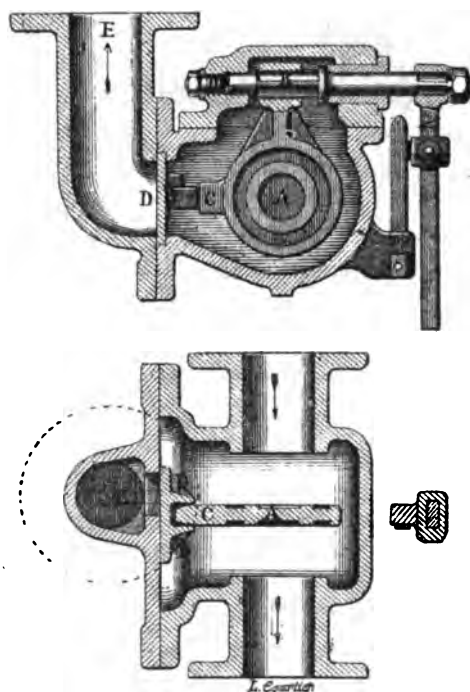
et 728. — Clapet obturateur de vapeur Vaultier (coupe et plan).
